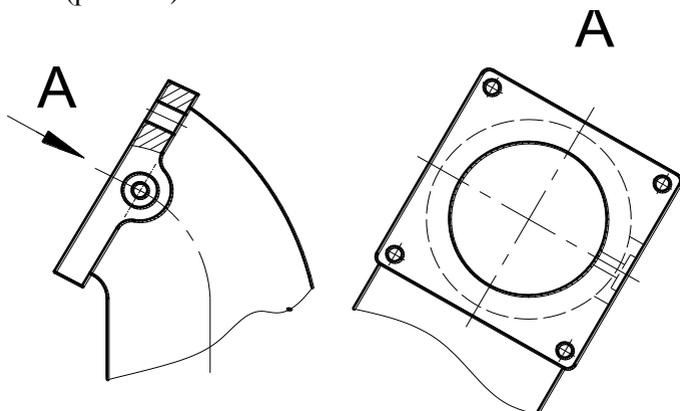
Расположение дополнительного вида на свободном месте поля чертежа
